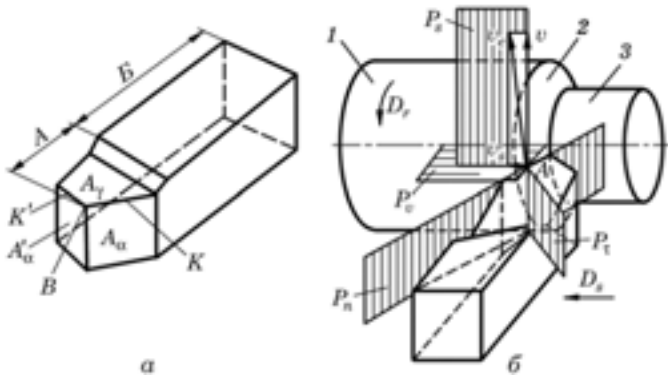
Елементи прохідного токарного різця (а), поверхні заготовки та координатні площини (б)
